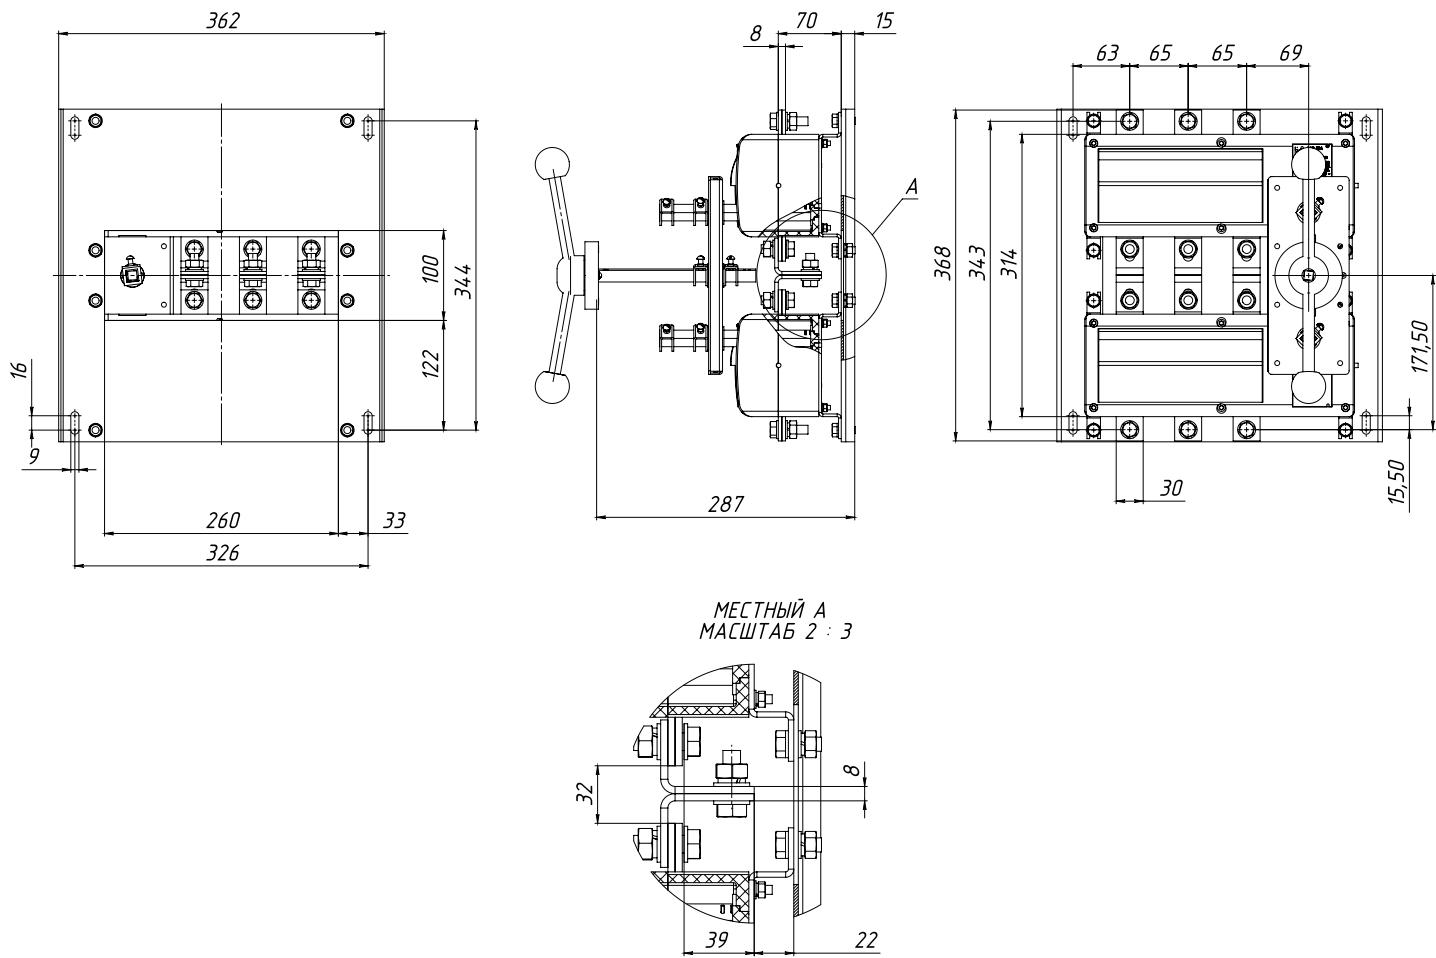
Выключатель-разъединитель ВНК-37-71130-32 УХЛЗ
